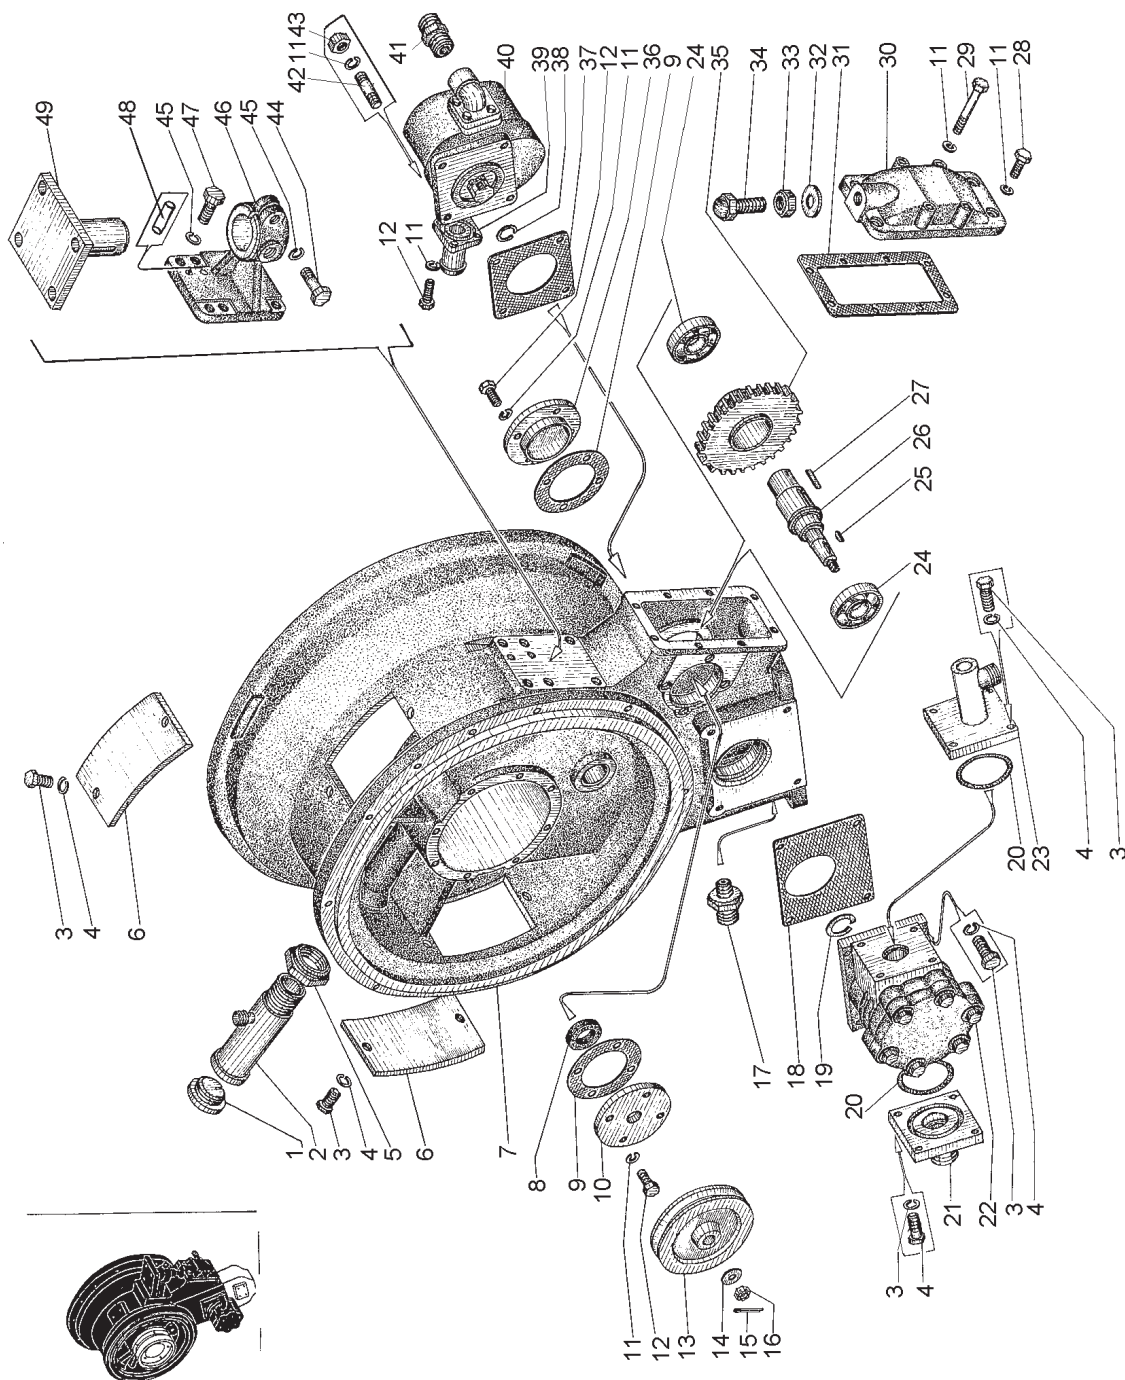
Редуктор промежуточный (ДЗ-98.10.06.000-09)
